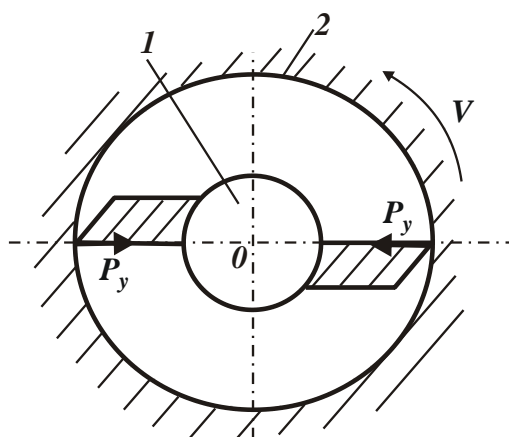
Схема обработки отверстия: 1 – осевой многолезвийный инструмент; 2 – обрабатываемая деталь.
